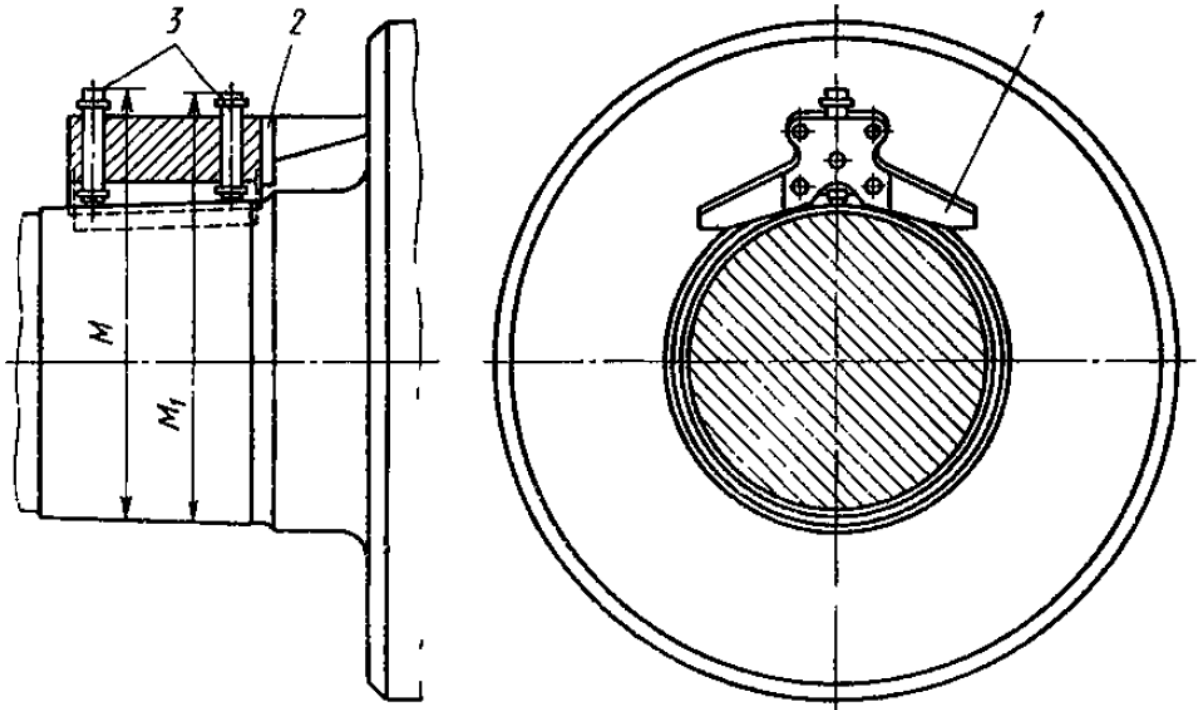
Схема контролю конусної шийки під підшипник великого діаметра.
